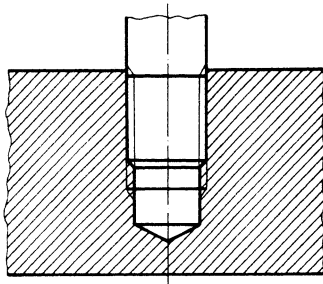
Zusammengebaute Gewindeteile, nutzbare Gewindelänge
